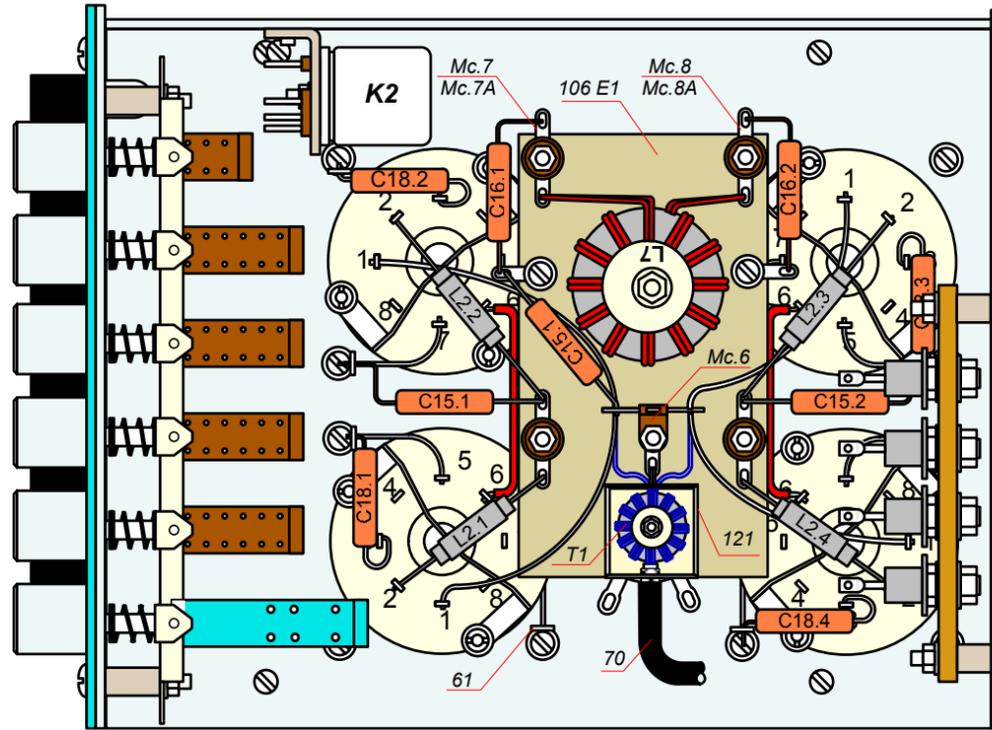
F. Сборочный чертёж усилителя DVA-300F (3 ГУ-50). Вид сверху со снятой верхней крышкой.
